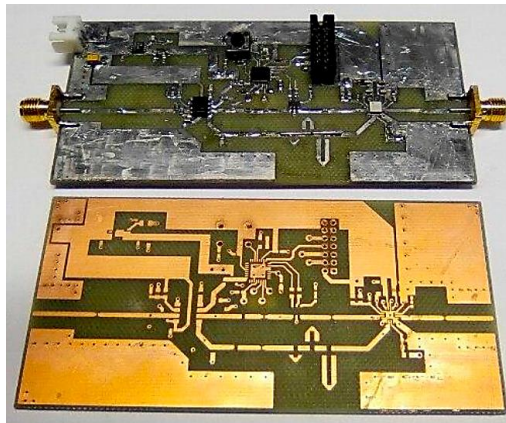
Виготовлена і зібрана друкована плата
